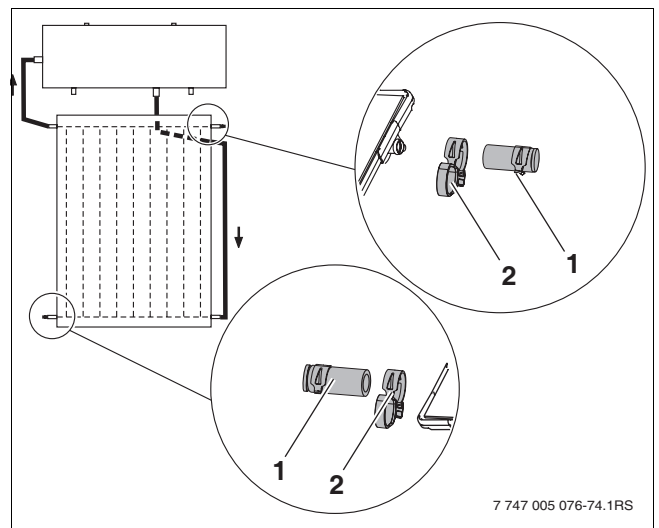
Abraçadeira de mola com anel de retenção e no estado montado no tampão cego pré-montado.
